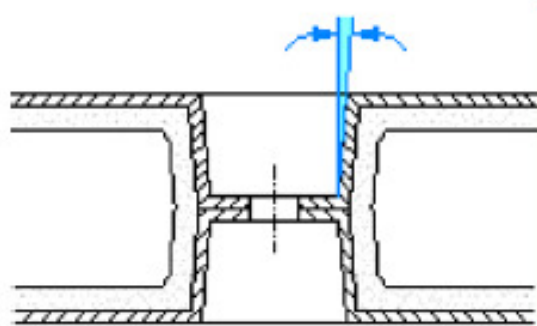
22 - Oggetto forato e sezione del relativo stampo
